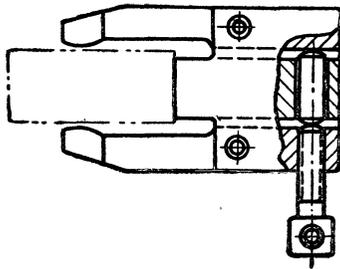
Комбинированный зажим для зажатия двух цилиндрических деталей.
